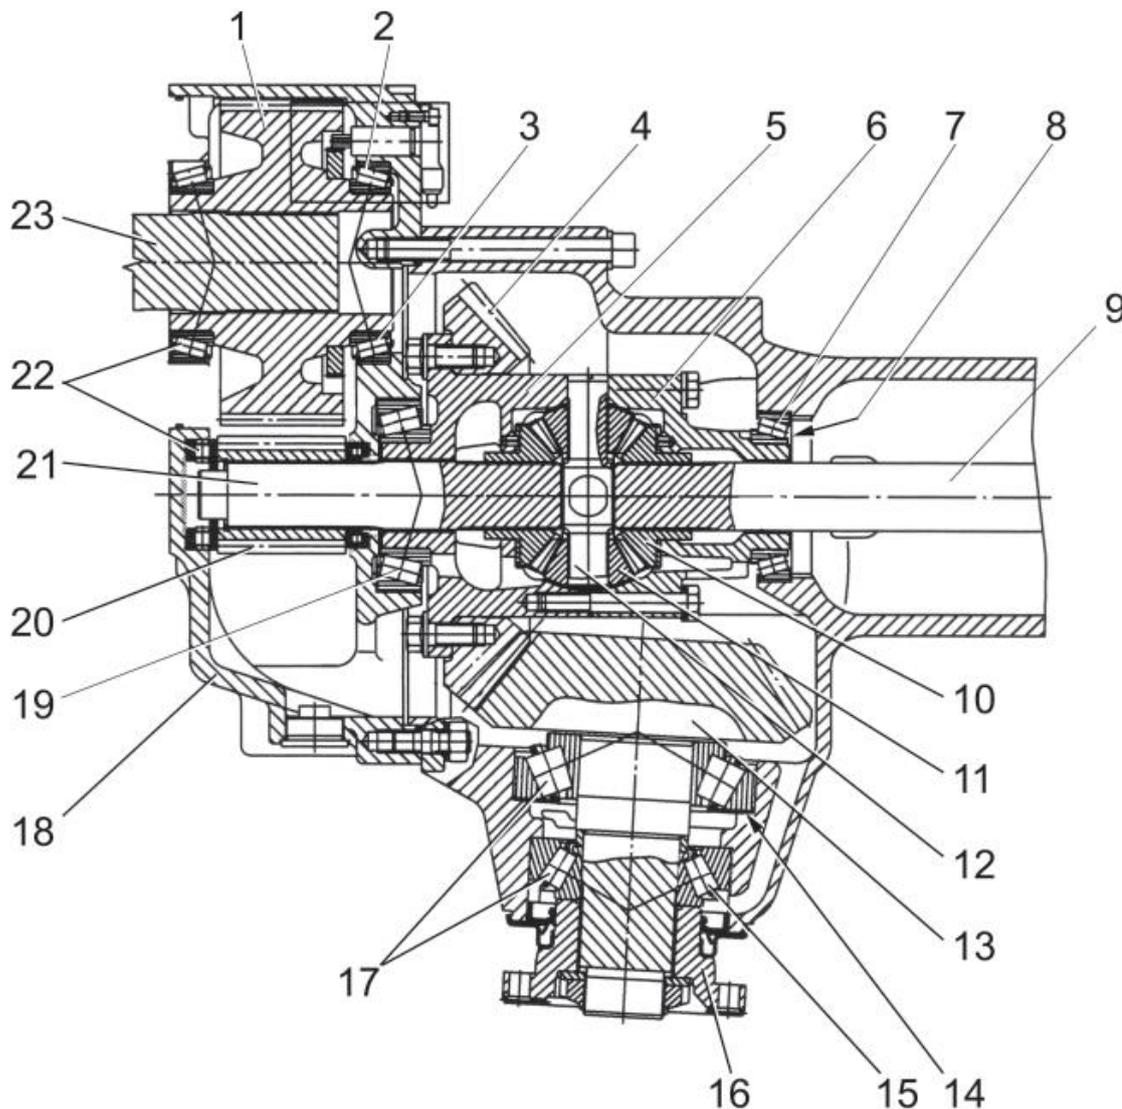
Главная передача (центральный конический редуктор, дифференциал) и колесный редуктор
